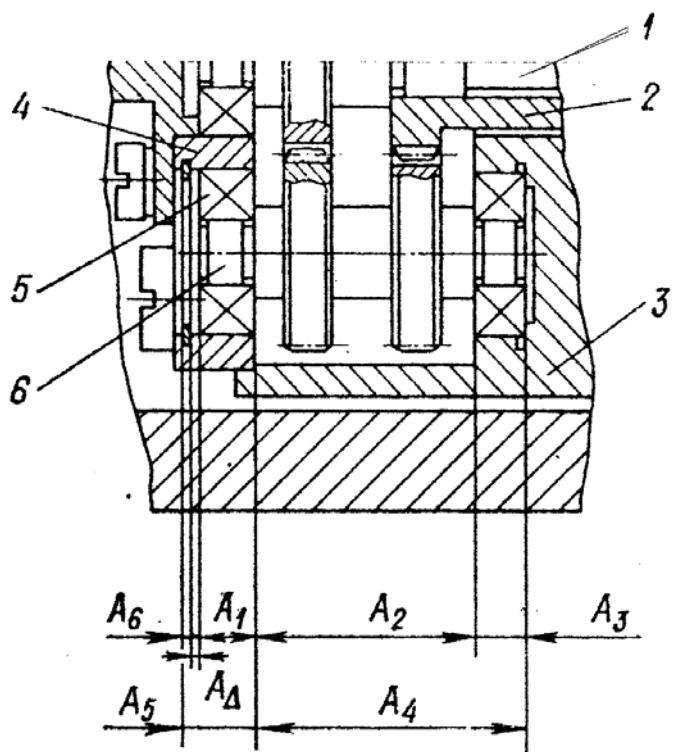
Узел подшипникового соединения: 1 – вал; 2 – колесо; 3- корпус;
